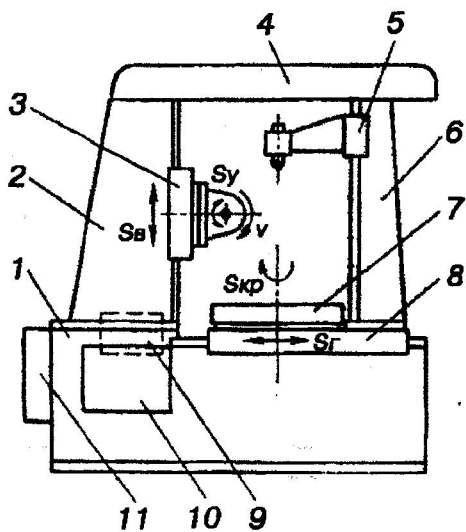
Загальний вигляд зубофрезерного верстата
